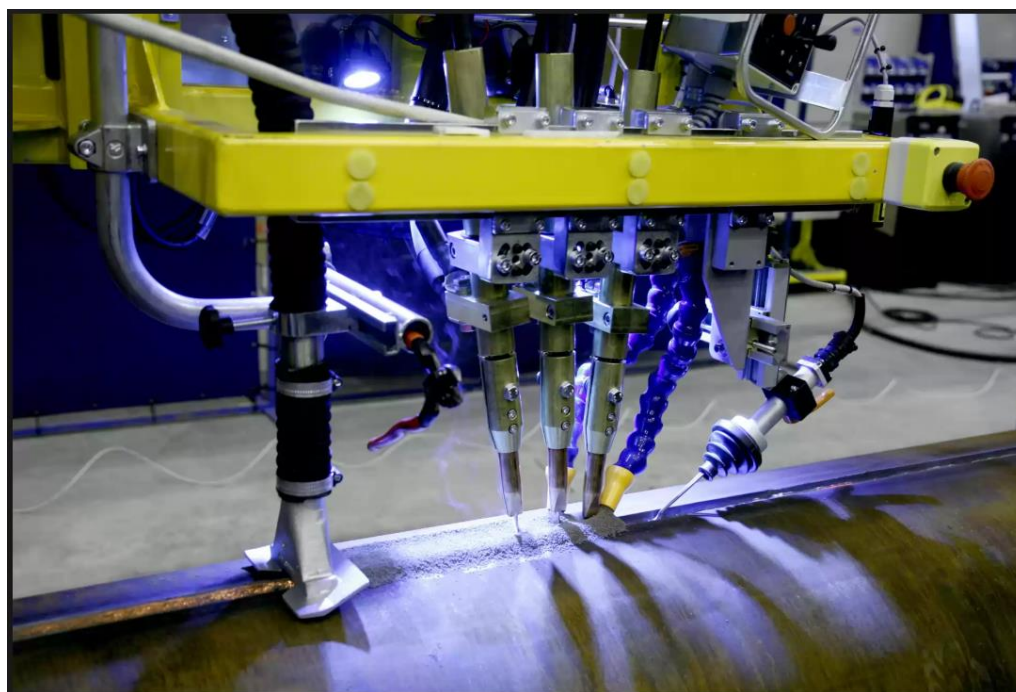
10 – Soldagem externa com arco submerso de uma tubulação
